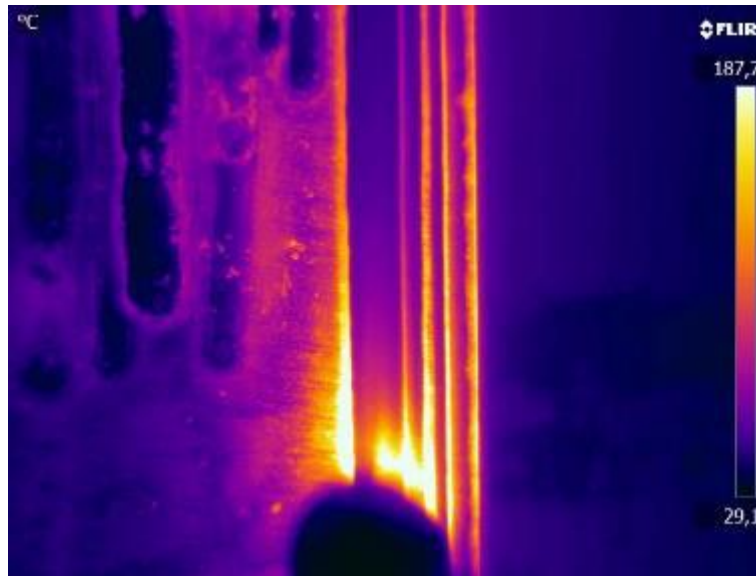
Imagen termográfica de un cordón de soldadura sin defectos a nivel macroscópico.
